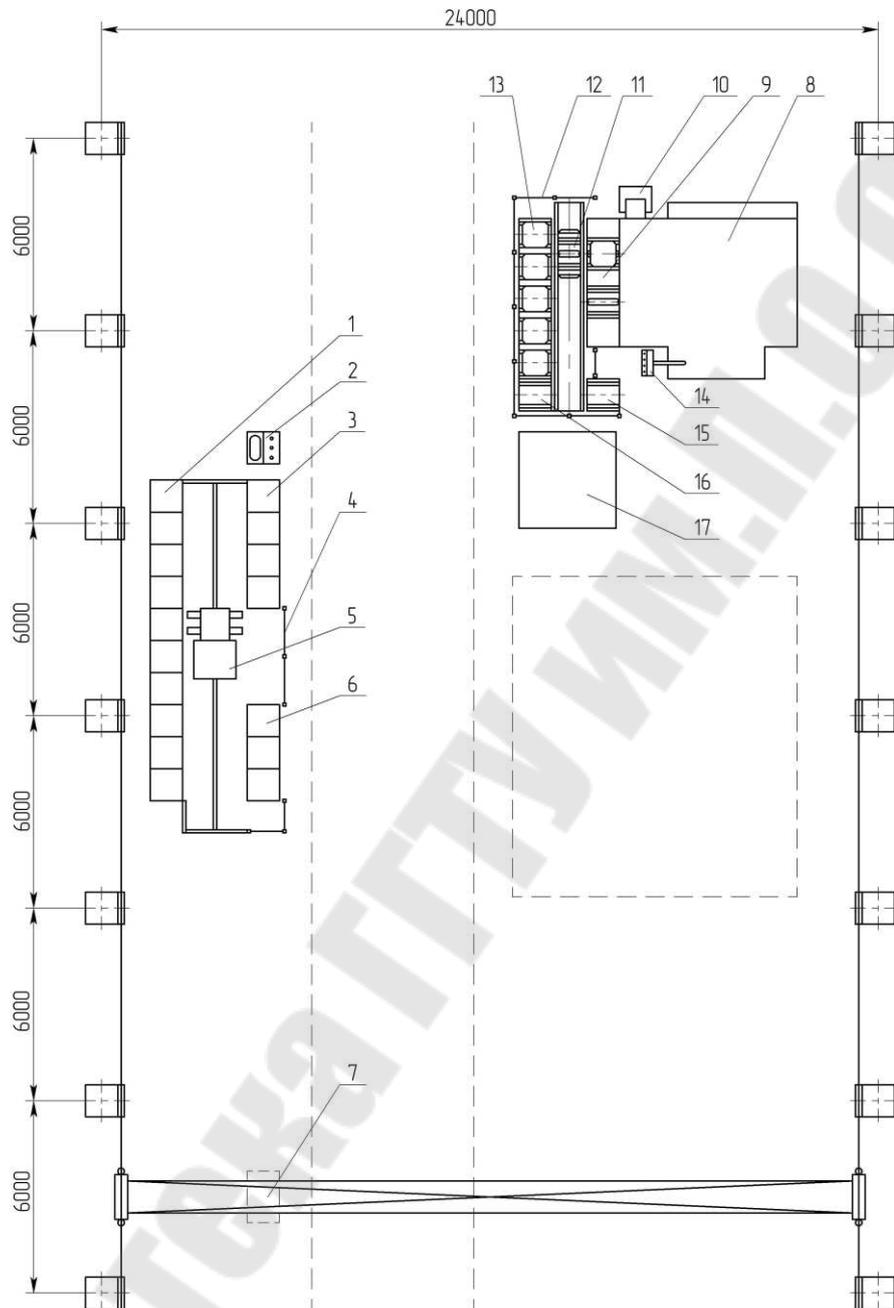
Пример планировки поточной линии, состоящей из АТК для обработки корпусных деталей.
